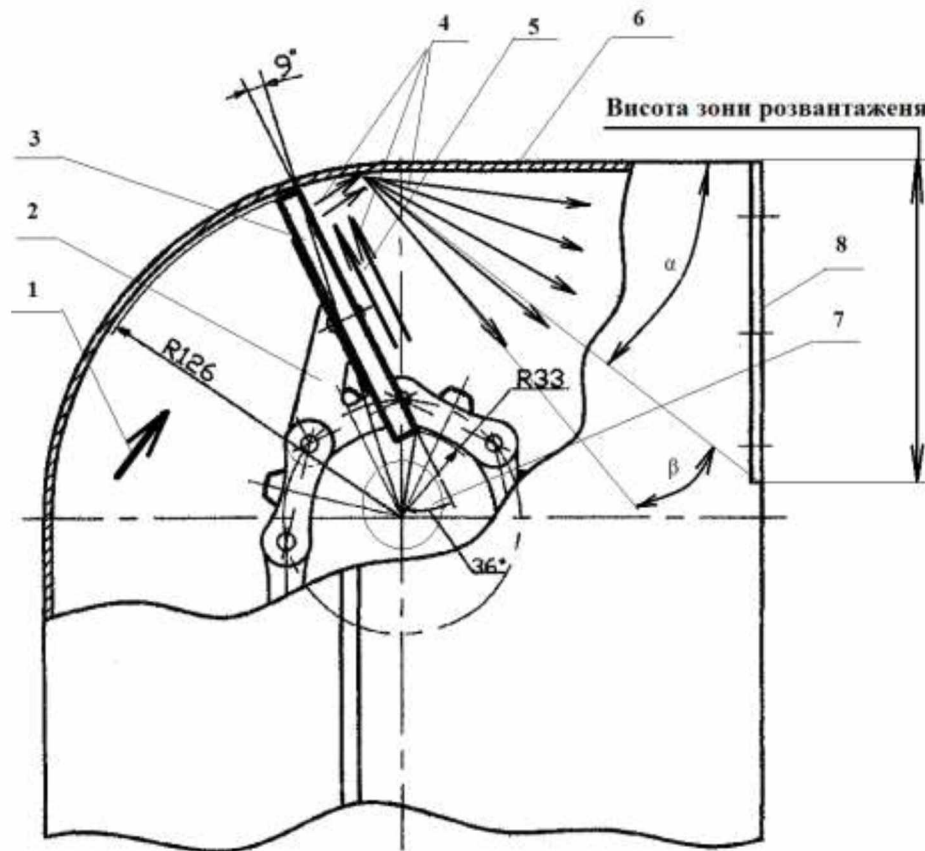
масштабована графічно-розрахункова схема верхньої частини скребкового елеватора по кресленням комбайна КЗС-9-1 «Славутич»: 1- корегований напрям руху зерна в елеваторі; 2- основа- кріплення скребка до елеваторного ланцюга; 3- скребок; 4 – можливі напрямки сходження зерна зі скребка елеватора; 5 - напрям руху зернової порції під дією відцентрової сили; 6 – кожух, що утворює обмеження по траєкторії розвантаження зерна; 7 – вал та зірочка приводу несучого ланцюга елеватора; α – кут, зумовлений сектором розвантаження; β – кут, що описує умови виникнення зворотнього сипу зерна.
